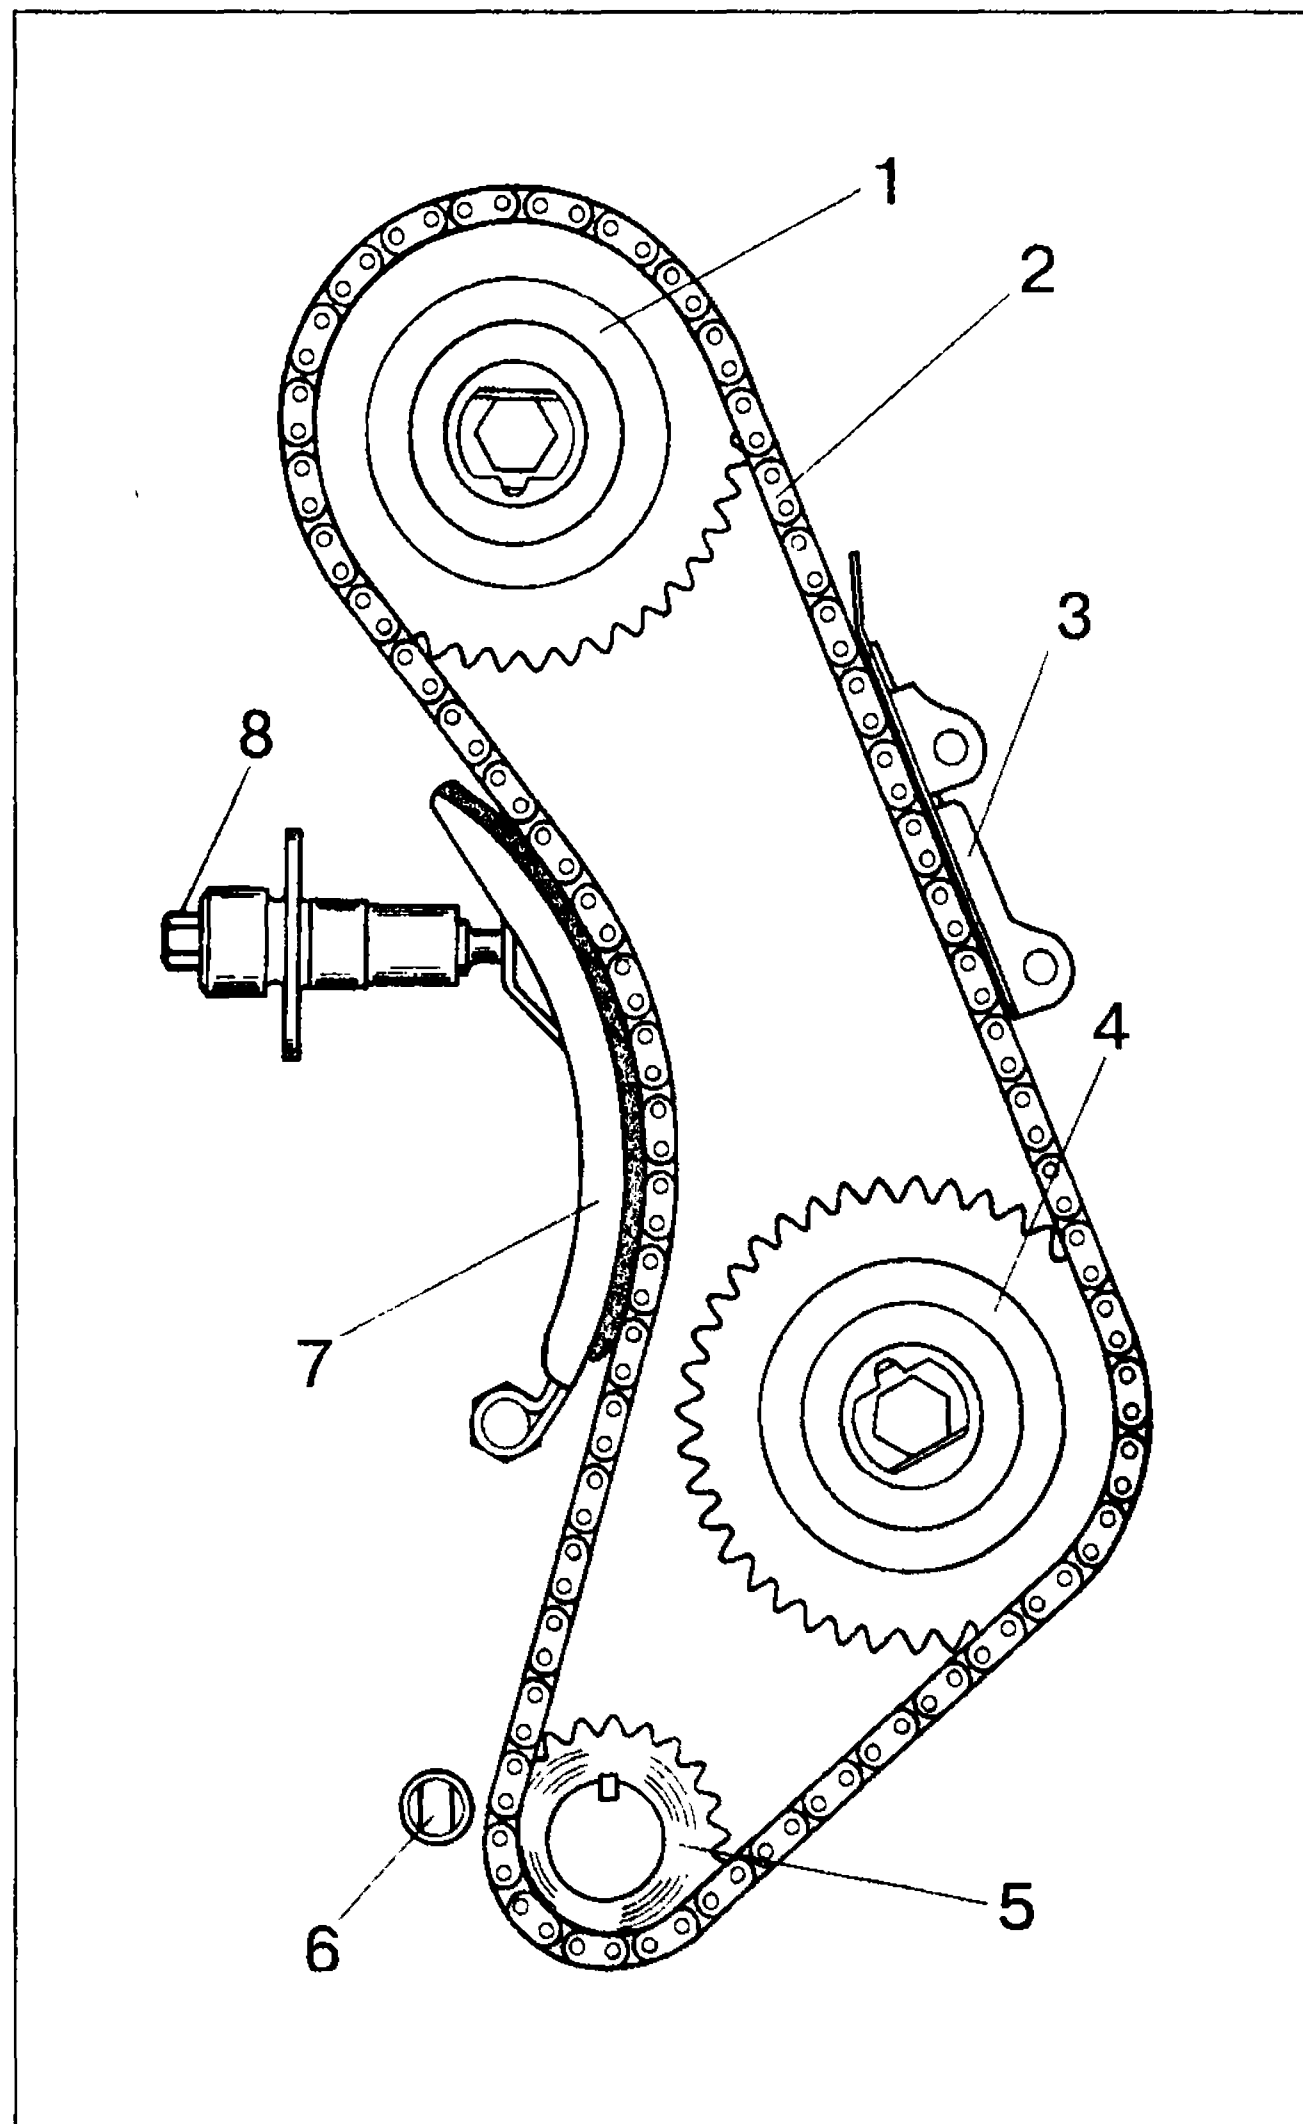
Схема механизма привода распределительного вала и вспомогательных агрегатов:
